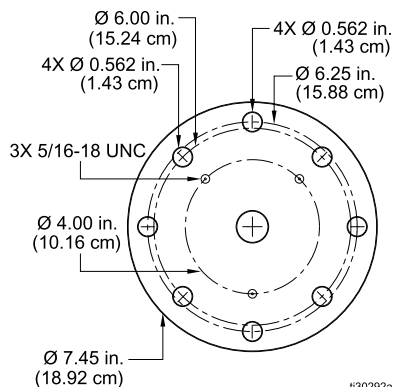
Dimensioni dei fori di montaggio dell'agitatore
